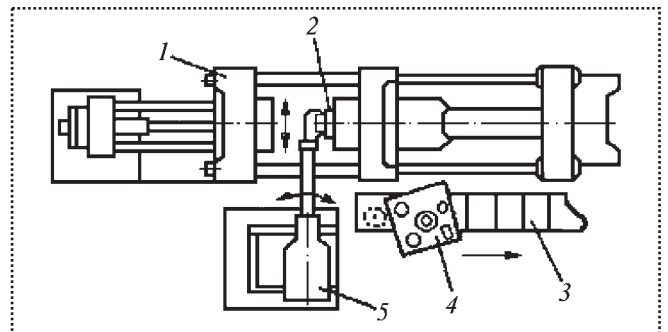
Робототехнический комплекс для производства заготовок методом литья под давлением:
